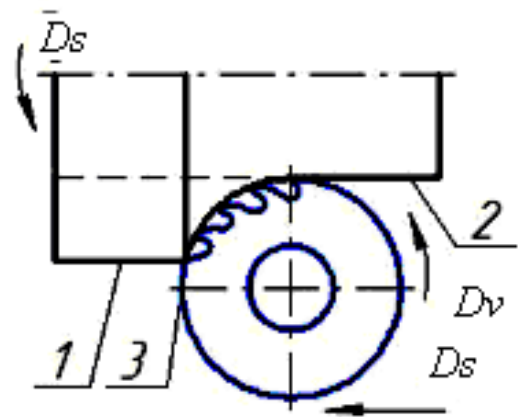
Кругове фрезерування. 1 - оброблена поверхня; 2 - оброблена поверхня; 3 - поверхня різання; D_r - головний рух; D_s - рух подачі.
